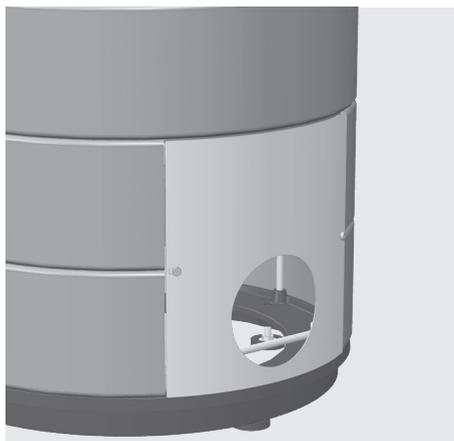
Plaque d'inspection sur la face arrière de l'appareil avec découpe pour le conduit
